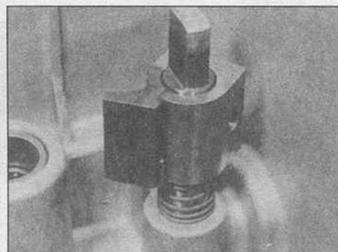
Расположения пружины фиксатора (Глава 8)
